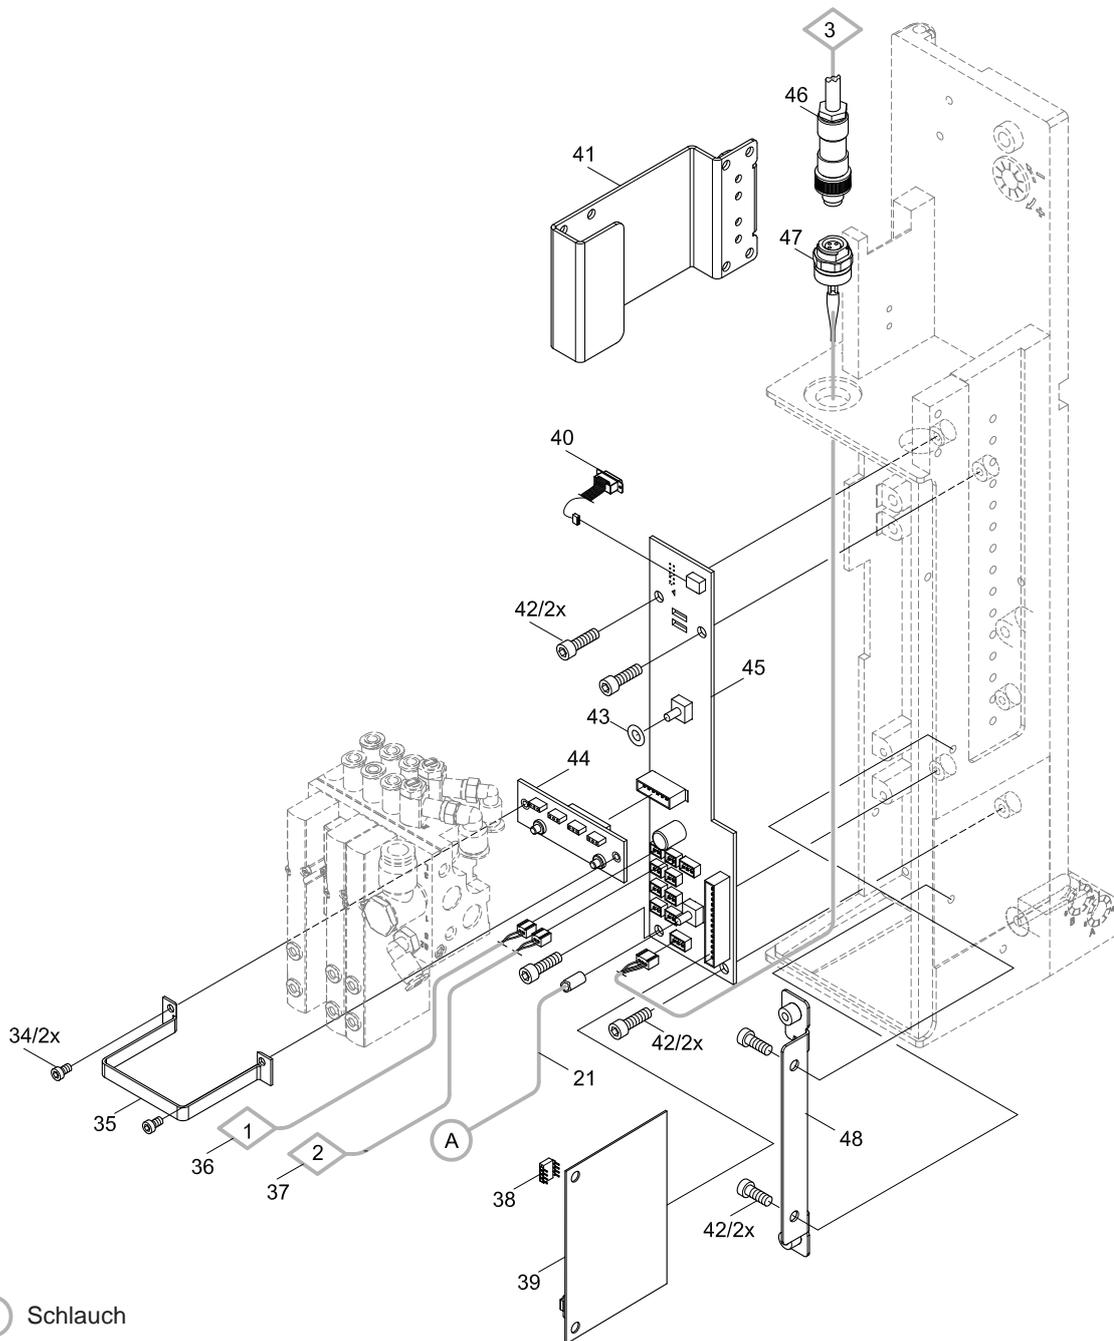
Elektronik Trägerbaugruppe - Ersatzteil
